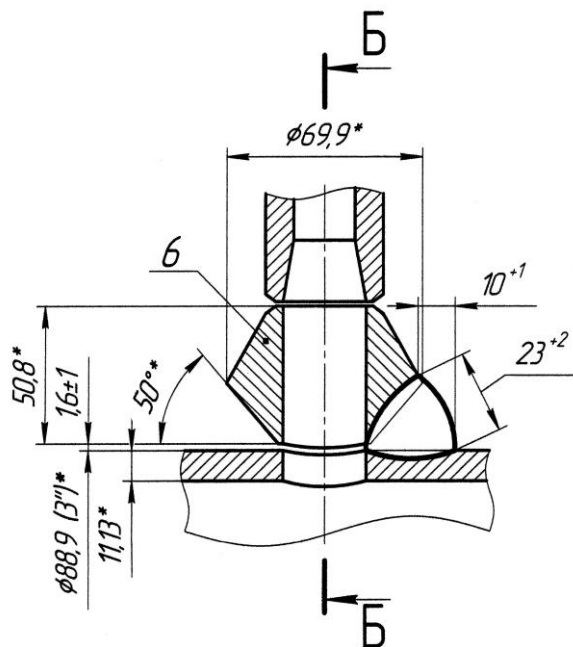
Общий вид соединения трубы 1 и бобышки 6.
